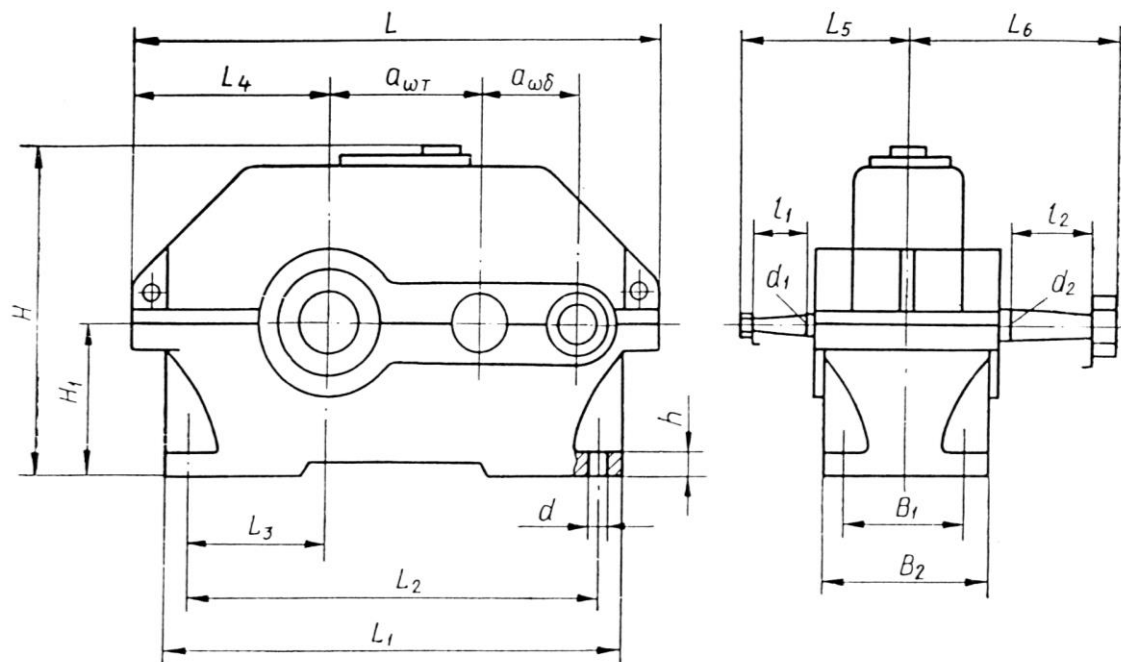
Основні розміри зовнішнього вигляду редуктора
